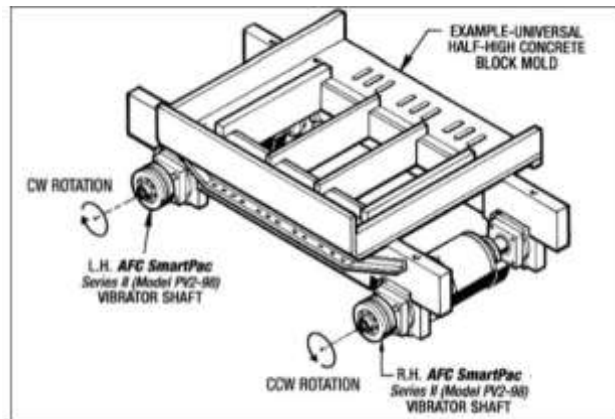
Bastidor del molde ensamblado (fuente: Besser Company)
